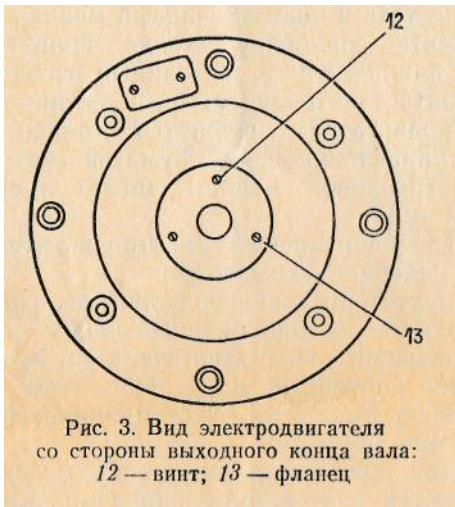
Вид электродвигателя со стороны выходного конца вала: 12 — винт; 13 — фланец
